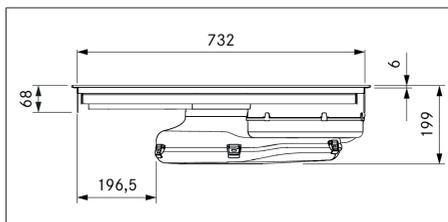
PURA dimensioni apparecchio vista frontale
